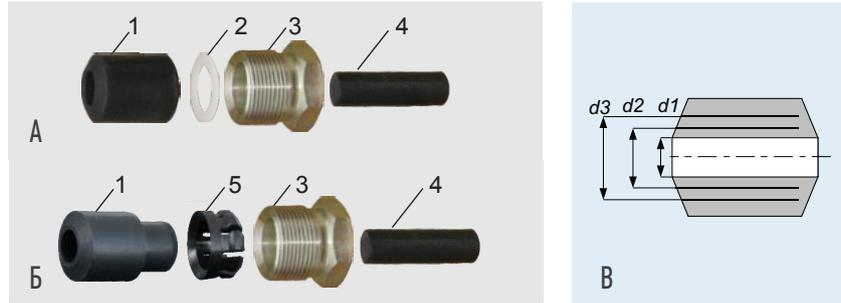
Устройство крепления металлорукава УКМ-10 (-12) для кабельного ввода "D12":
